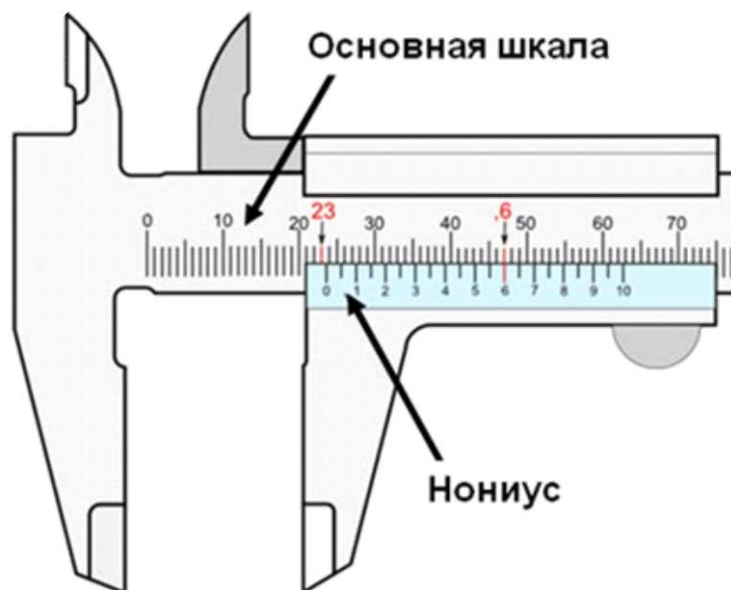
Основная и нониусная шкалы штангенциркуля
